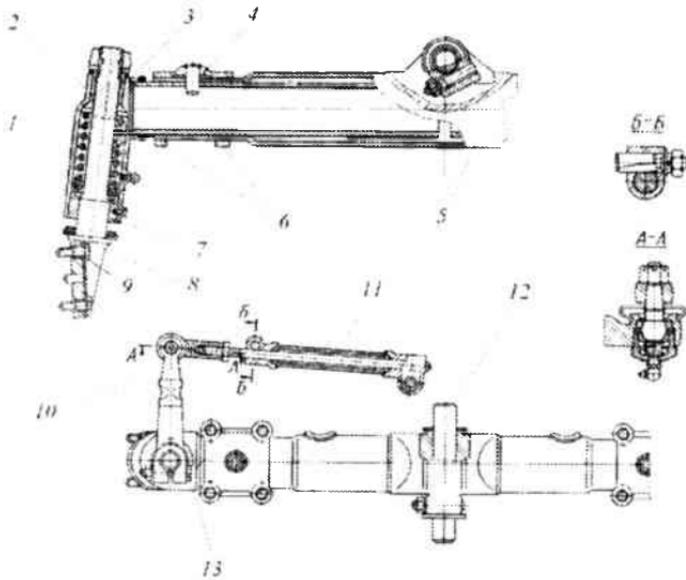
Передний мост универсально-пропашного трактора Т-40: 1 – шарикоподшипник; 2, 7 – втулки; 3 – кронштейн; 4 – накладка со штифтом; 5 – балка; 6 – хомут; 8 – шкворень; 9, 13 – болты; 10 – поворотный рычаг; 11 – поперечная рулевая тяга; 12 – ось качения
